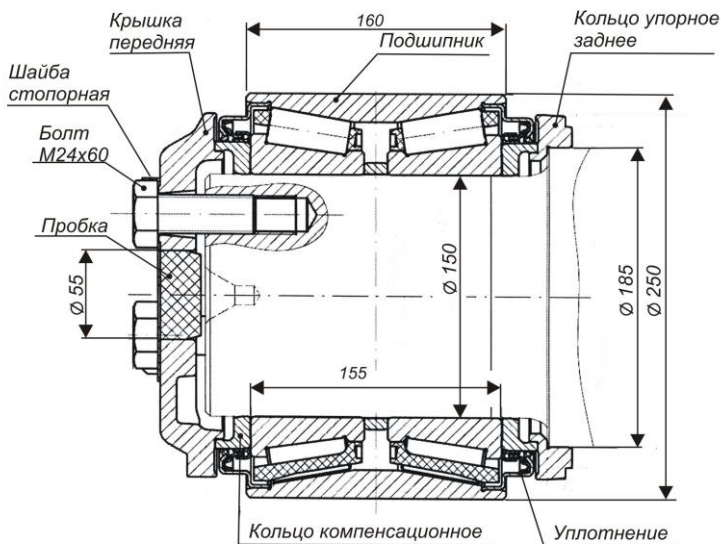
Конический подшипниковый узел под адаптер с базовым подшипником в габаритных размерах $150 \times 250 \times 160$ мм марки «Brenko» для оси типа РВ2Ш
